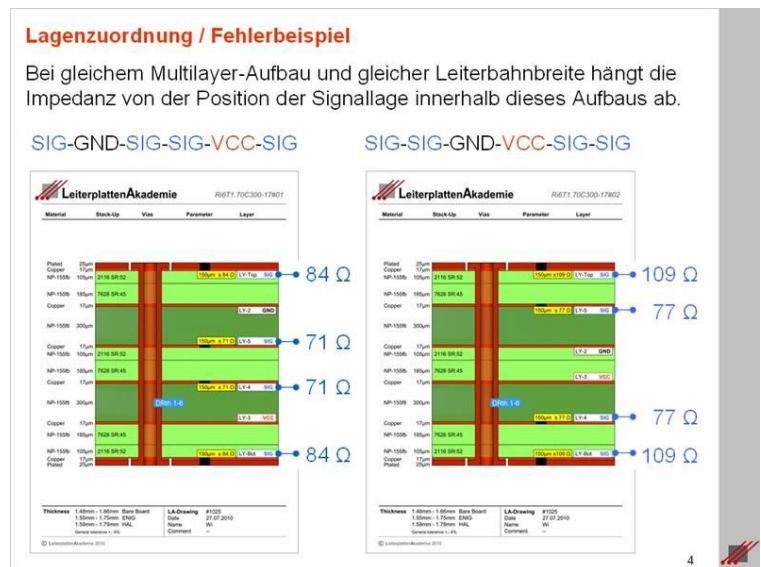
Impedanzfehler bei falschem Lagenaufbau
